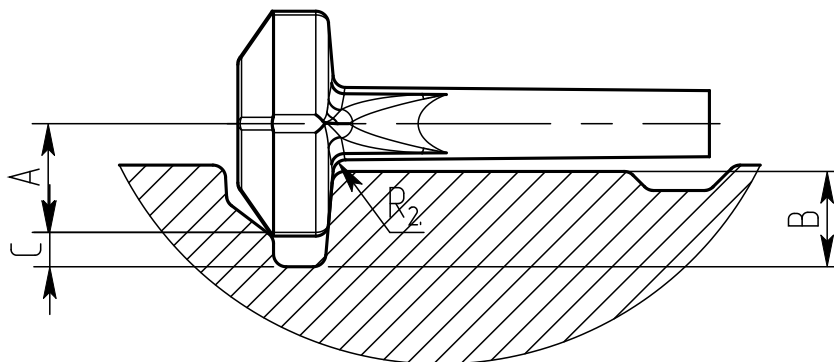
Требуемое расположение заготовки в ручье окончательного штампа с обозначением размеров. A – расстояние от оси до угла заготовки; B – глубина ручья; C – расстояние от точки соприкосновения заготовки со штампом до наиболее глубокой точки ручья; R_2 – радиус в плоскости перпендикулярной плоскости разреза штампа.
